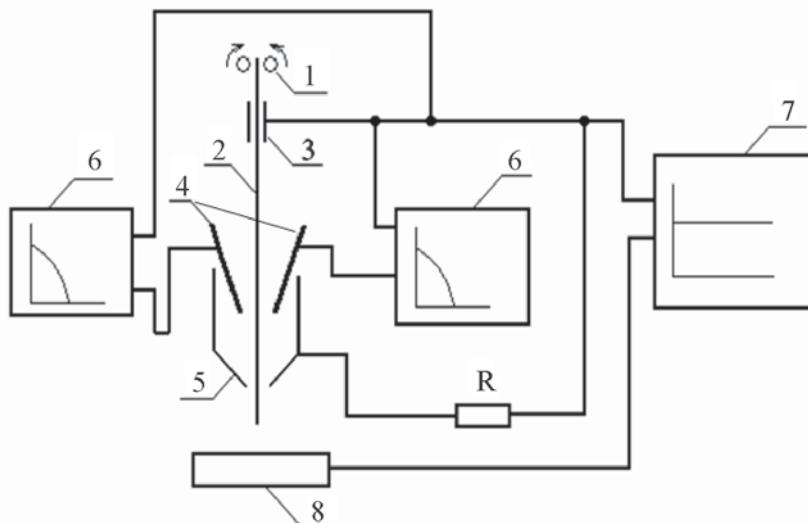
Схема установки для плазма-MIG наплавки порошковой лентой:
